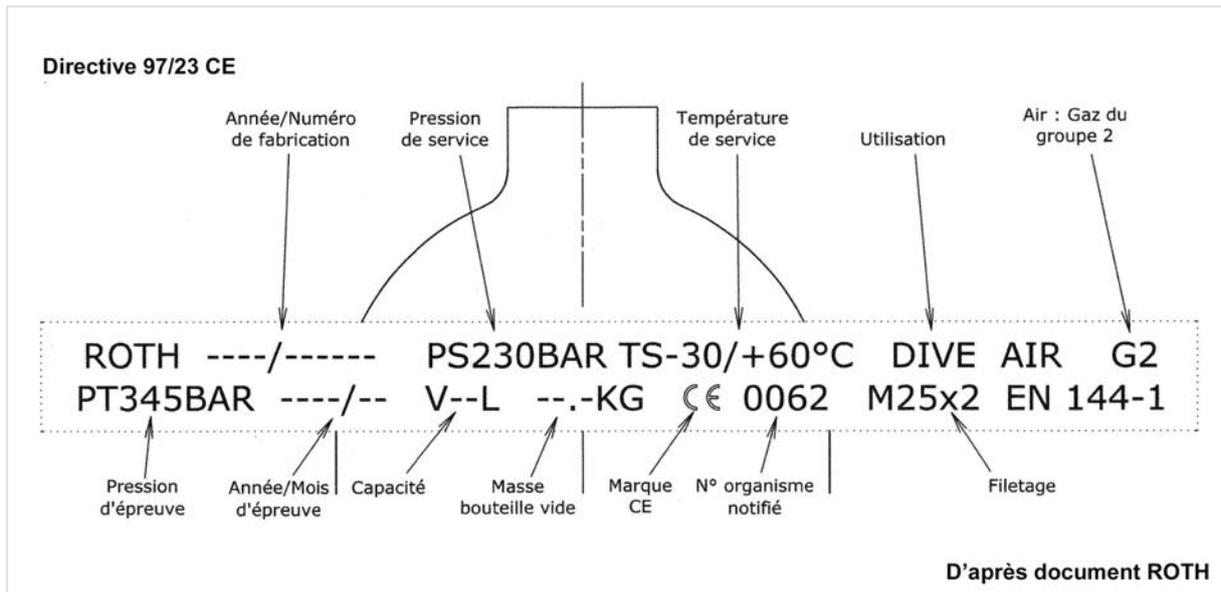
Plan suivant la directive 97/23 CE - Bloc AIR
